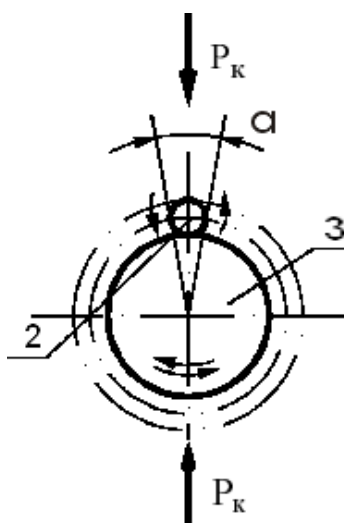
Схема работы игольчатого подшипника в крестовине карданного вала
